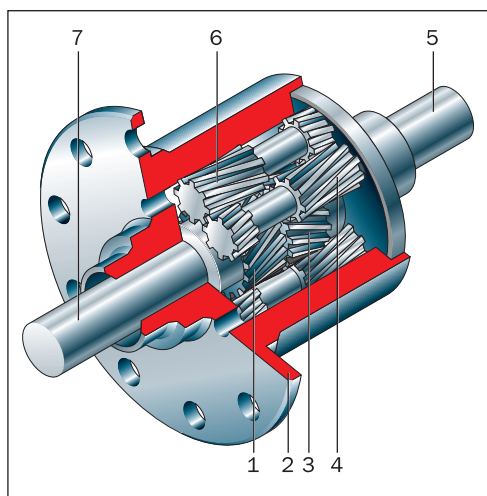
Межколесный дифференциал Torsen: 1, 3 — правая и левая полуосевые шестерни; 2 — корпус дифференциала; 4 — сателлит, связанный с правой полуосевой шестерней; 5, 7 — выходные валы дифференциала; 6 — сателлит, связанный с левой полуосевой шестерней
